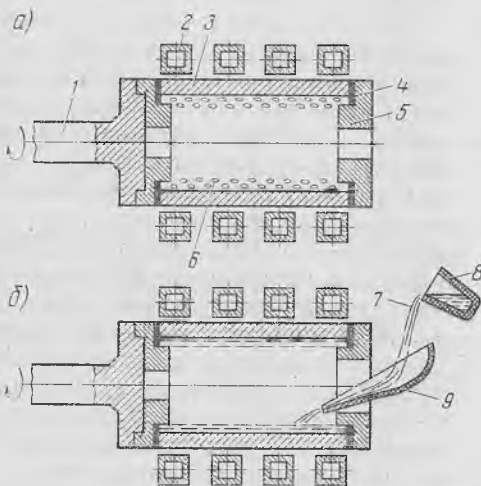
Принципиальная технологическая схема центробежной наплавки: а — присадочный металл в виде шихты; б — присадочный металл в виде расплава; 1 — шпиндель центробежной машины; 2 — индуктор ТВЧ; 3 — наплавляемая деталь; 4 — прокладки; 5 — крышка с отверстием; 6 — шихта; 7 — присадочный сплав; 8 — разливочный ковш; 9 — лоток из огнеупорного материала
